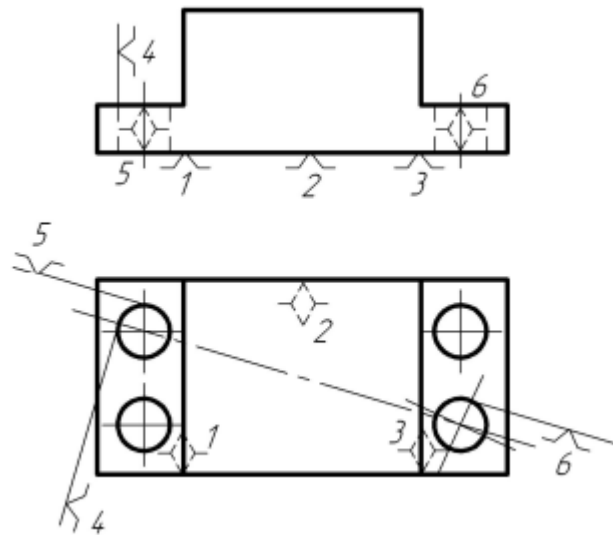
Установлення заготовки на площину і два пальці (круглий і зрізаний)
